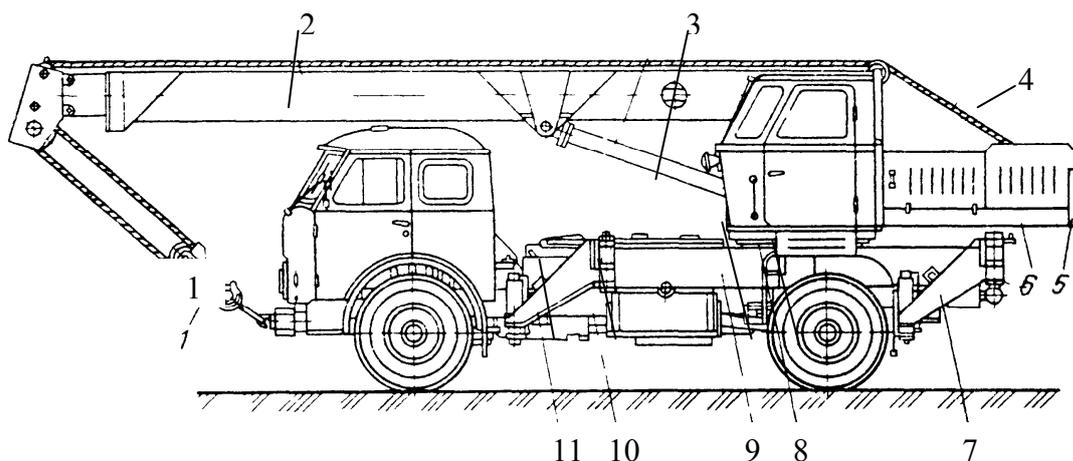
Автомобильный кран с жесткой подвеской рабочего оборудования: 1 – крюковая подвеска; 2 – телескопическая стрела; 3 – цилиндр подъема стрелы; 4 – канат; 5 – противовес; 6 – поворотная рама; 7, 11 – выносные опоры; 8 – опорно-поворотное устройство; 9 – рама; 10 – ходовое устройство (шасси автомобиля)
